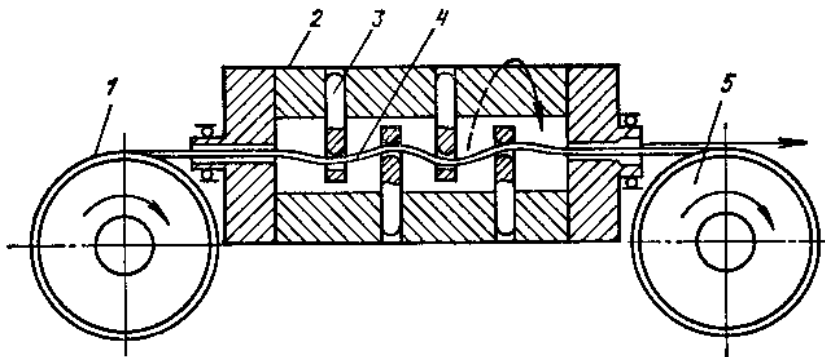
Принципова схема установки для виправлення дроту: 1 – барабан з мотком дроту, який виправляється; 2 – обертовий корпус; 3 – регульовані стрижні з філь'єрами; 4 – дріт у зоні виправлення; 5 – барабан натягу і транспортування дроту.
